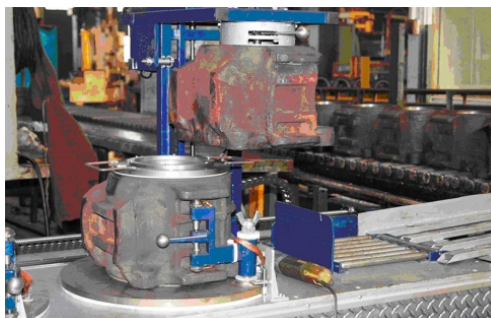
Очистка внутренней поверхности корпуса вагонной буксы
